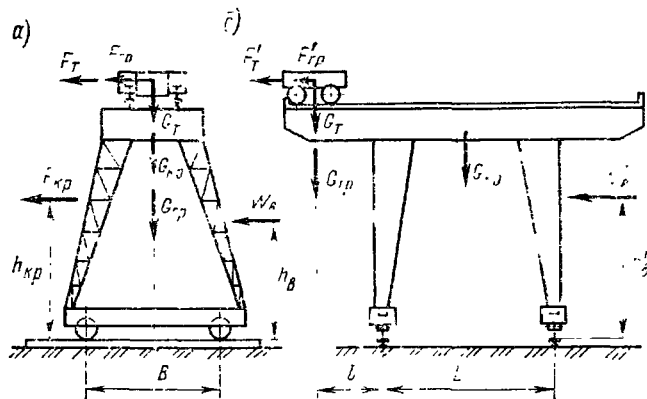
Схема к определению грузовой устойчивости козловых кранов вдоль (а) и поперек (б) подкранового пути
